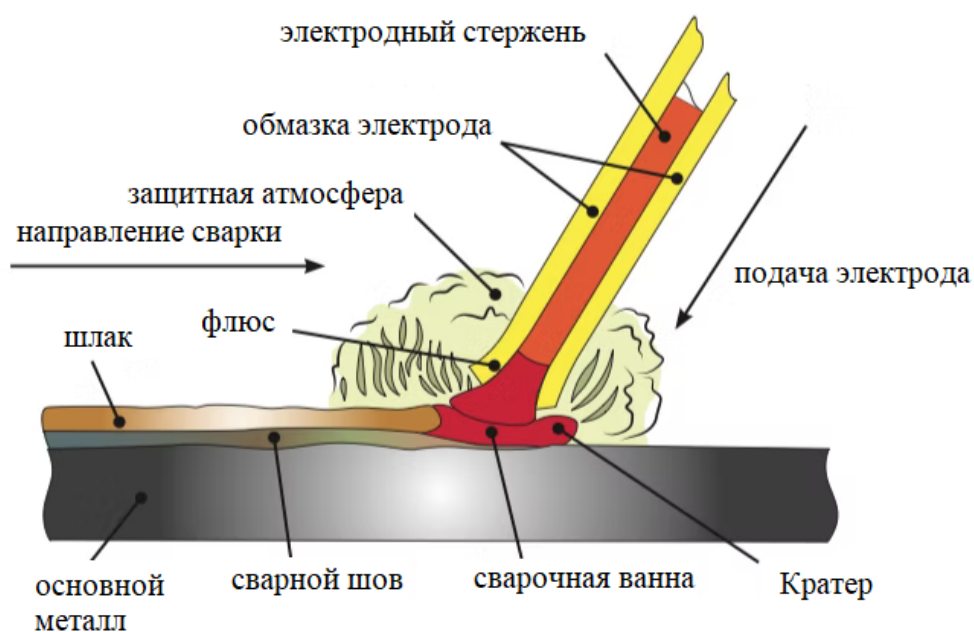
Схема выполнения ручной дуговой сварки
